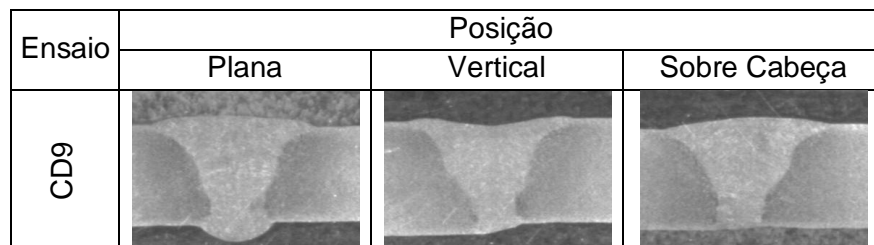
Macrografia dos ensaios soldados na progressão de soldagem ascendente (como escala adotar espessura da chapa 5,5 mm).
